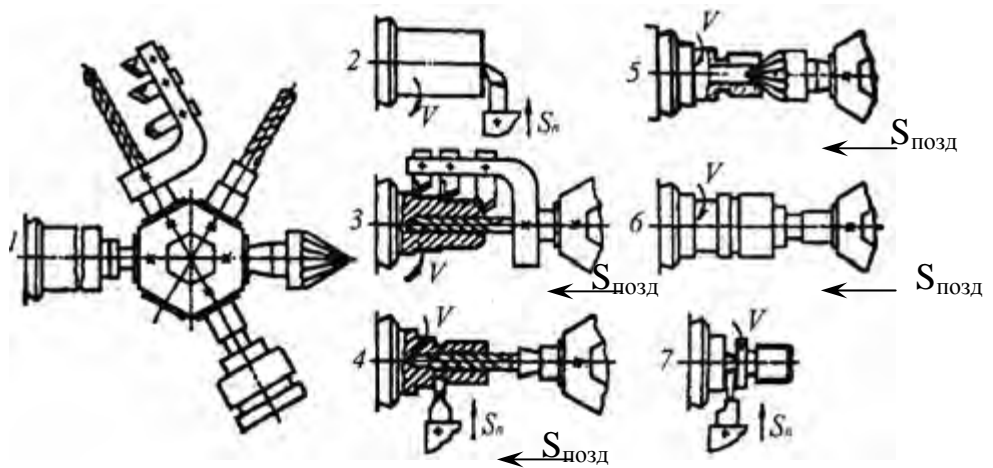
Схеми оброблення поверхонь заготовок на токарно-револьверних верстатах
